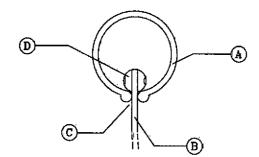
SEZIONE STRUTTURA TUBOLARE
